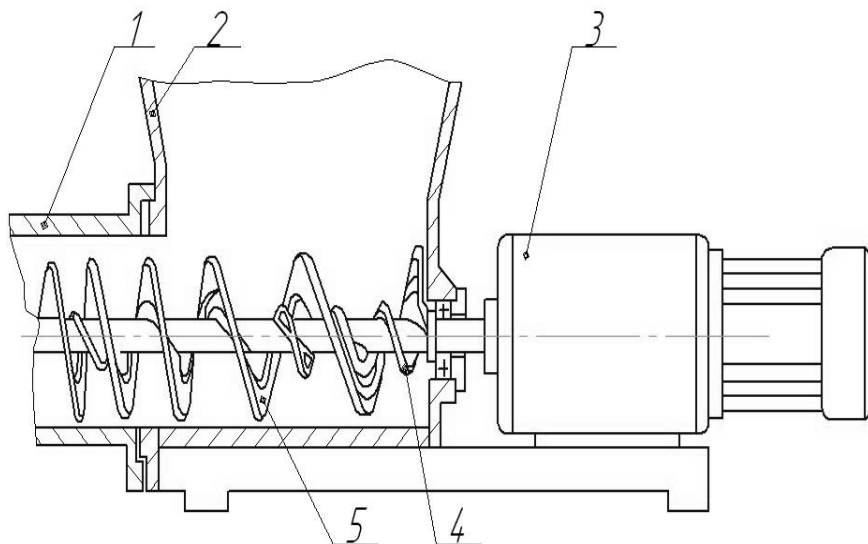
Транспортуючий механізм: 1 – корпус; 2 – бункер; 3 – привід; 4 – внутрішня навивка шнека; 5 – стрічкова спіраль
